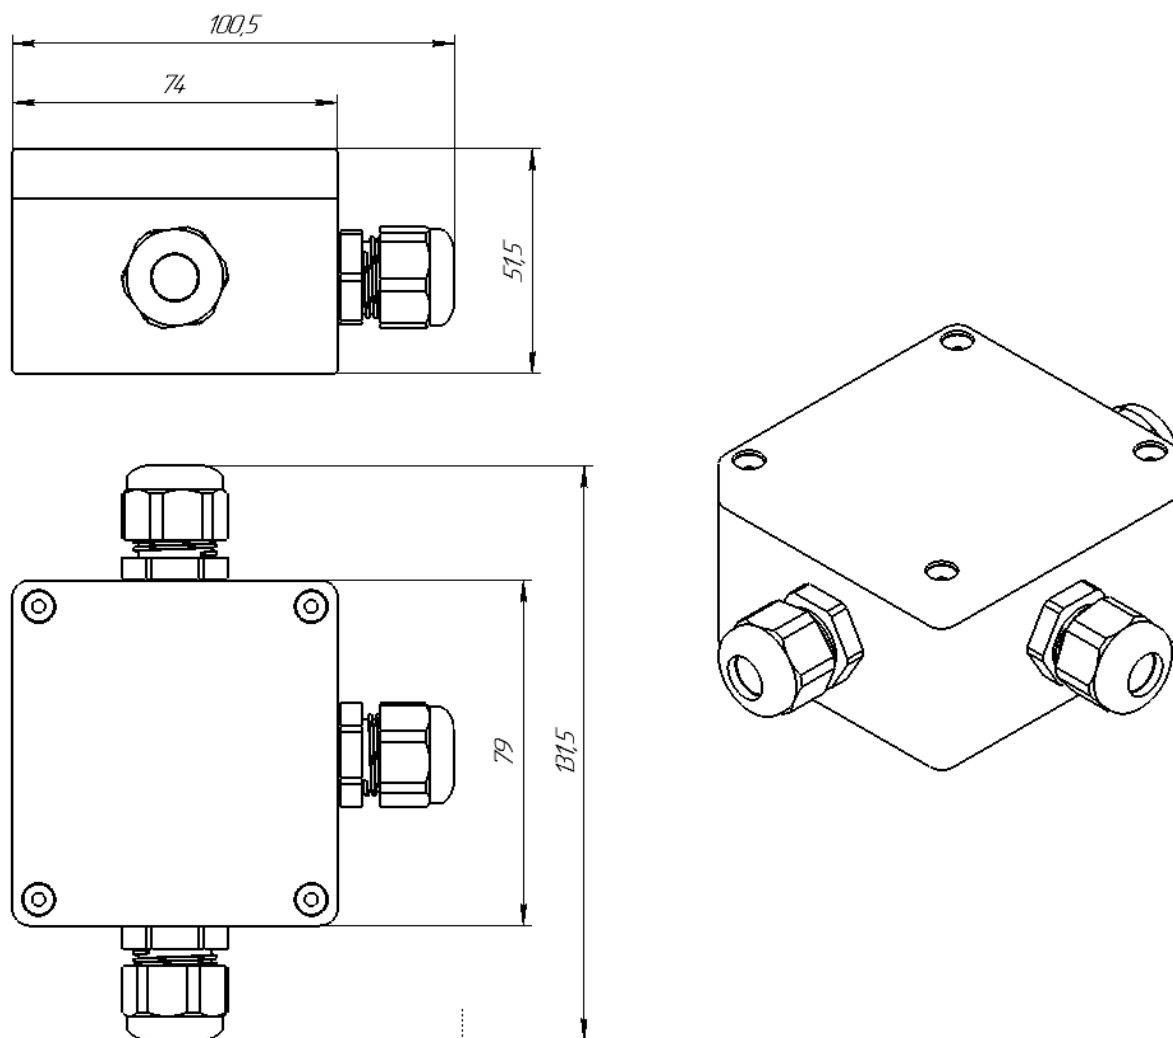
Габаритные и установочные размеры ПР-3УМ
